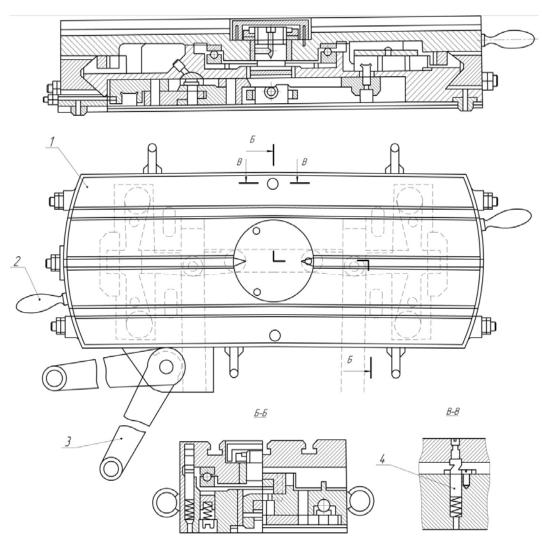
Поворотный двухпозиционный стол: 1 – планшайба; 2 – рукоятка поворота; 3 – рукоятка зажима; 4 – фиксатор
